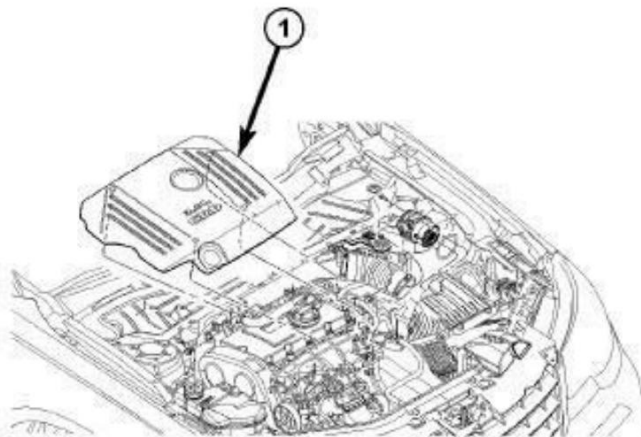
Tapa del motor: extracción e instalación Cortesía de CHRYSLER LLC
